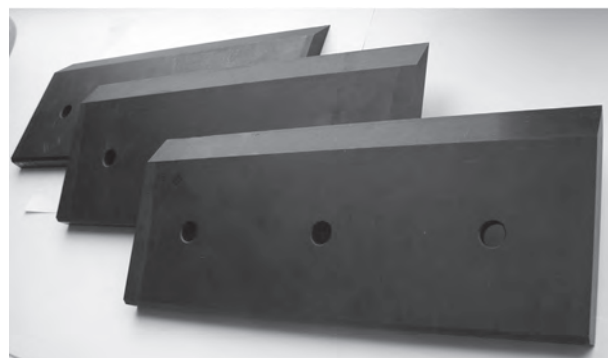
Опытный образец ножа для рубки щепы ФТИ5.001.1671
